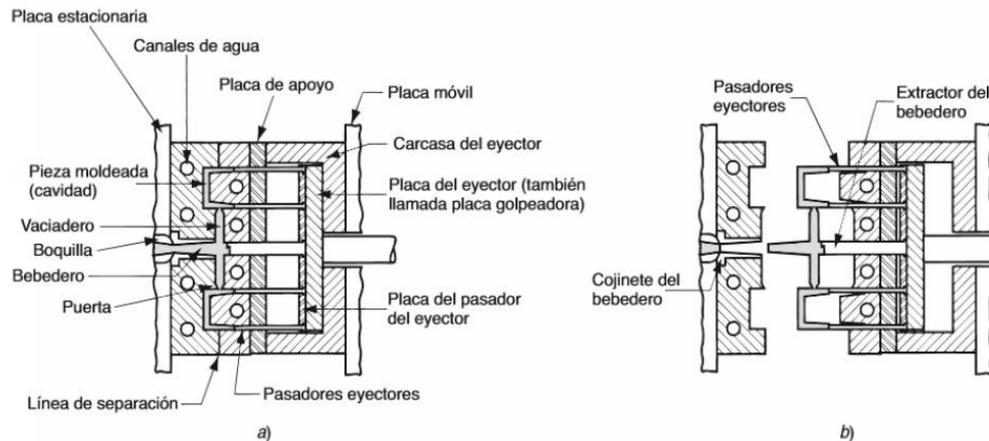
Molde de dos placas a) cerrado – b) abierto [13]
